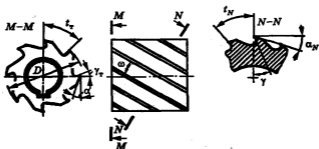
Геометрические параметры режущей части цилиндрической фрезы
